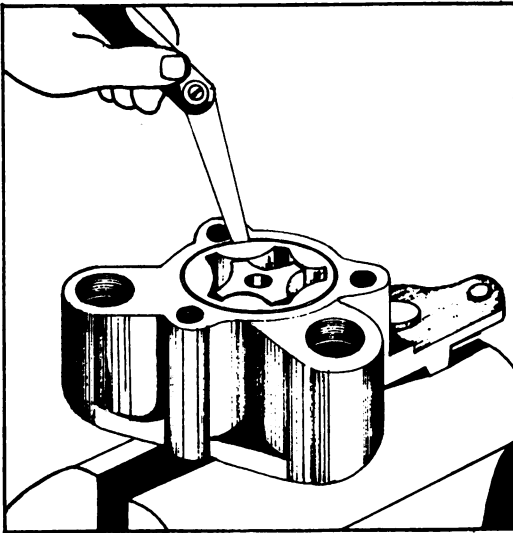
Luz lateral entre los engranajes y la caja de la bomba de aceite.
